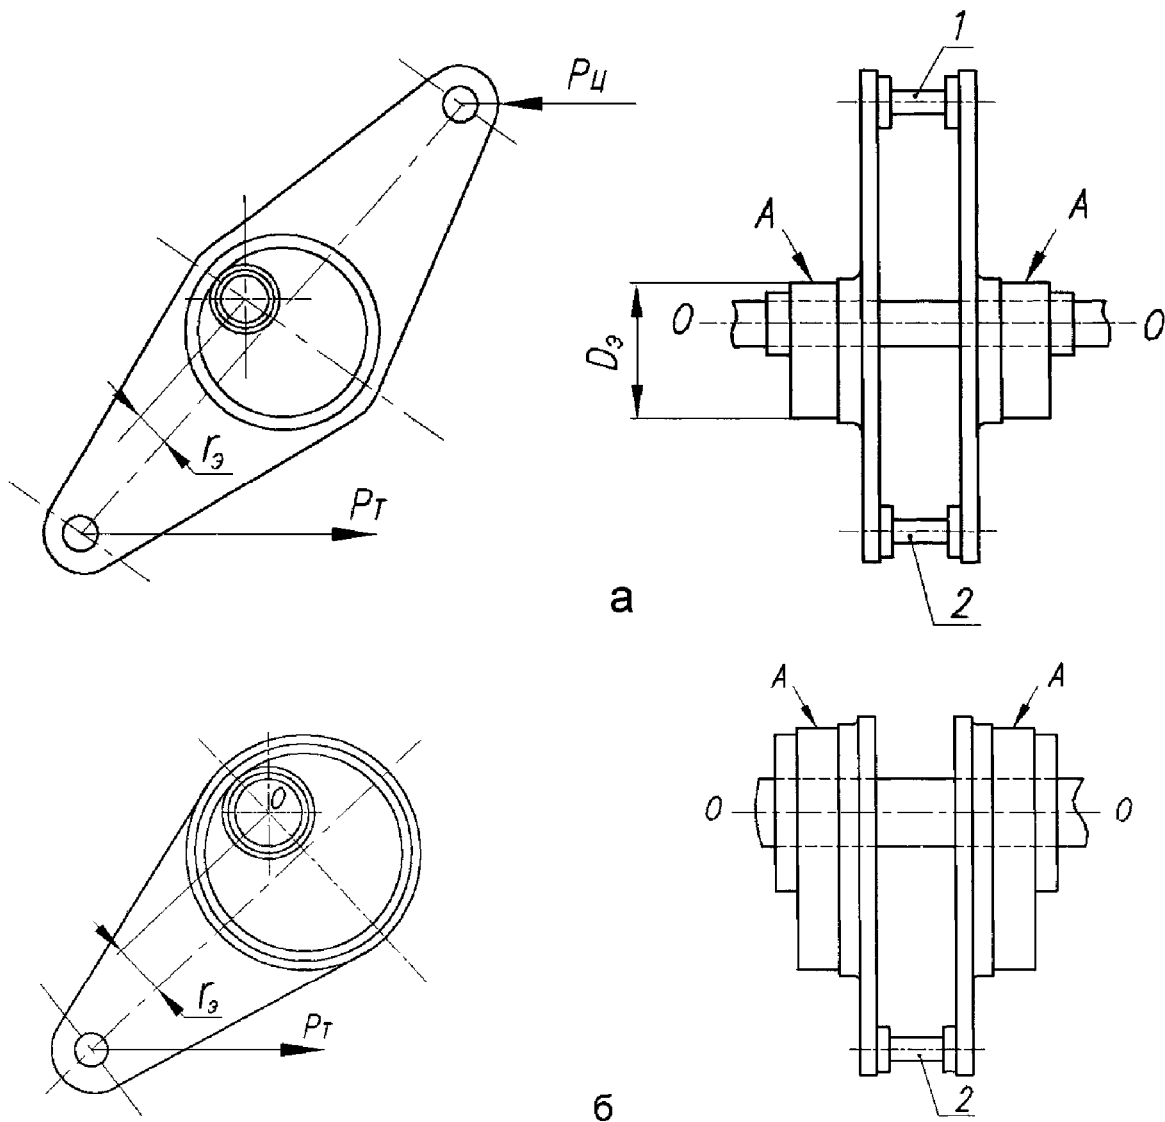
Схема установки эксцентриковых втулок с рычагами на оси ходовых колёс:
